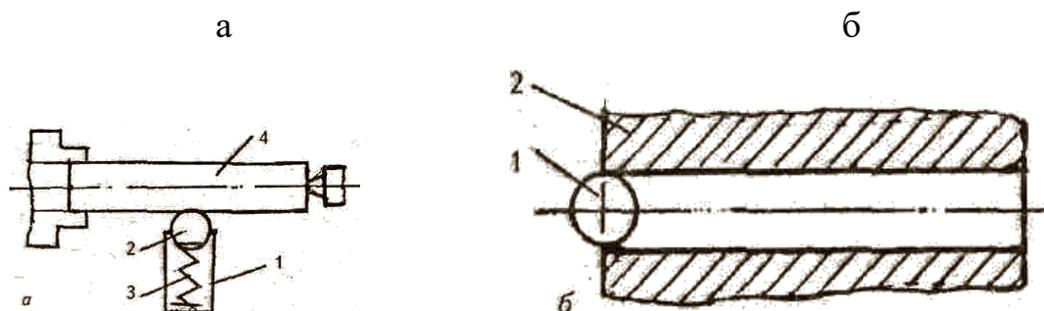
Схема упрочнения поверхности: а — накаткой: 1 - оправка; 2 - шарик; 3 - пружина; 4 - деталь;
